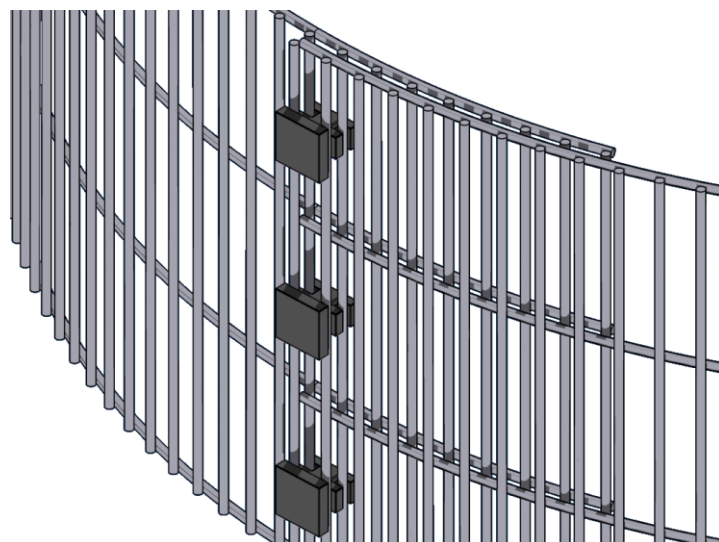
Montageplan der Schutzeinrichtung RT
